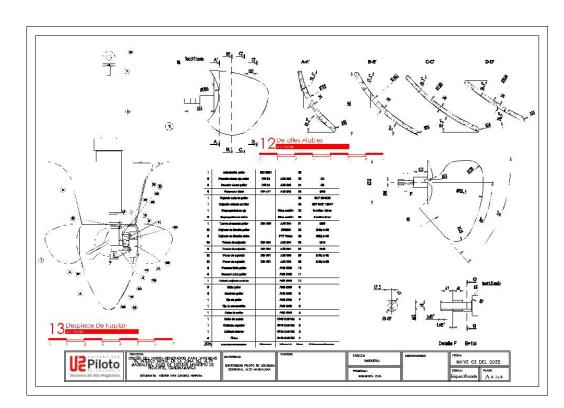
Plano A4-4, Plano de Despiece de la Turbina Kaplan.
